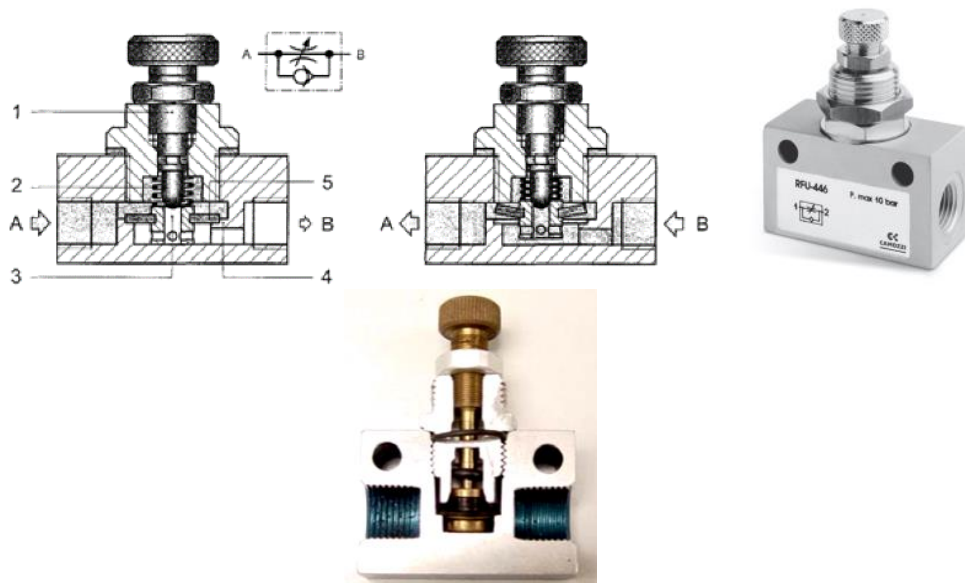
Пневмодрессель с обратным клапаном (конструкция и условное графическое обозначение на схемах): 1 – регулировочный винт; 2 – пружина; 3 – дросселирующее отверстие; 4 – седло; 5 – тарельчатый обратный клапан
